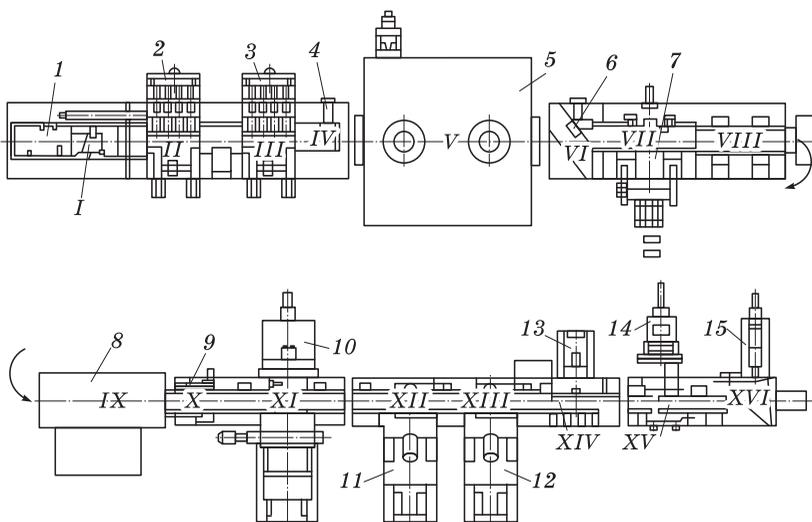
Автоматическая линия сборки головки блока цилиндров (I...XVI — позиции сборки)
